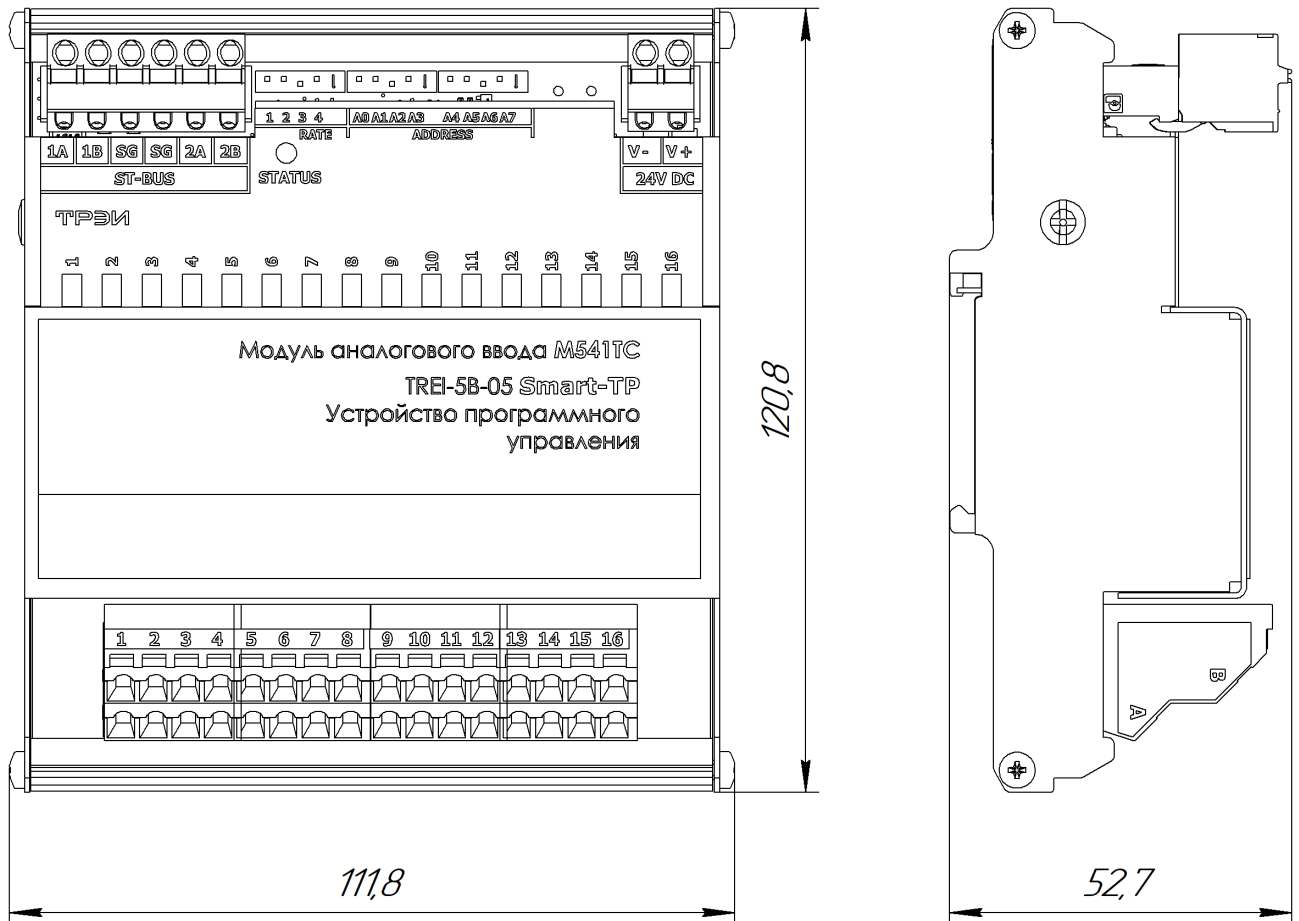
Чертеж общего вида M541TC с указанием габаритных и присоединительных размеров
